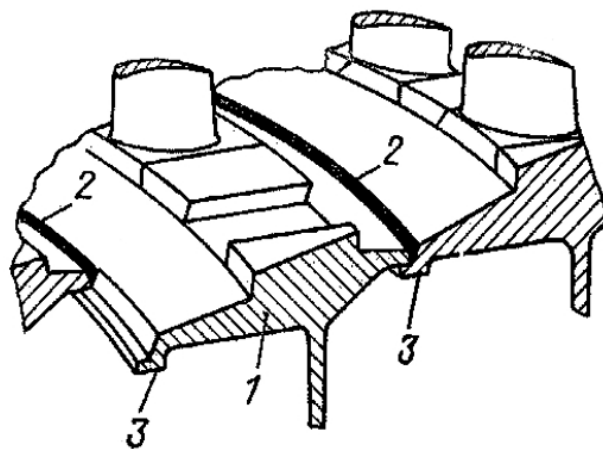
Соединение секций ротора, выполненное сваркой.
